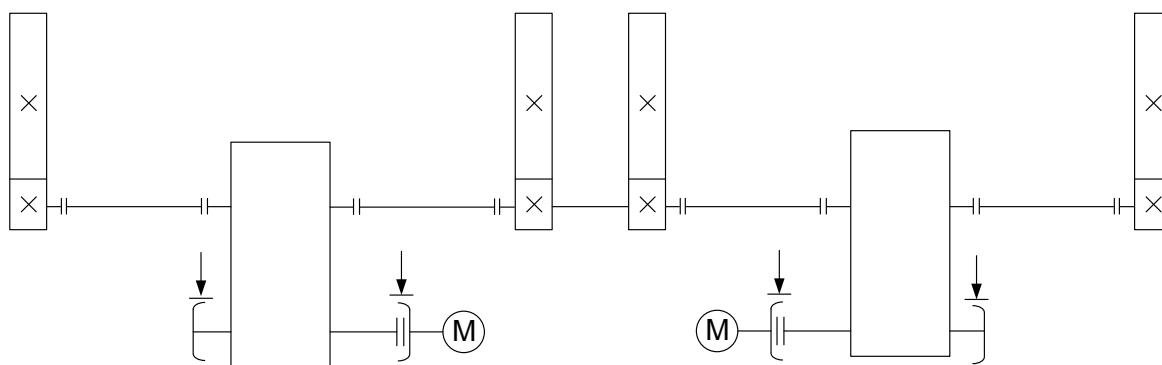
Кинематическая схема вагоноопрокидывателя
